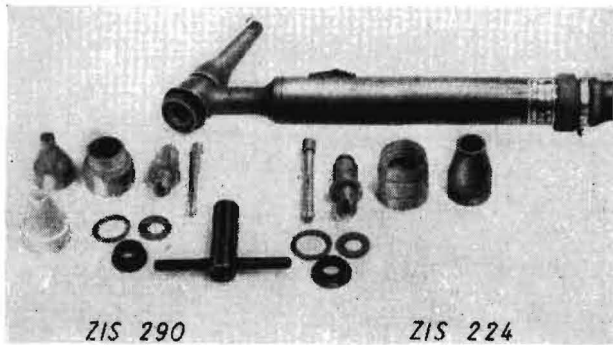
WIG-Schweißbrenner ZIS 290 und ZIS 224
